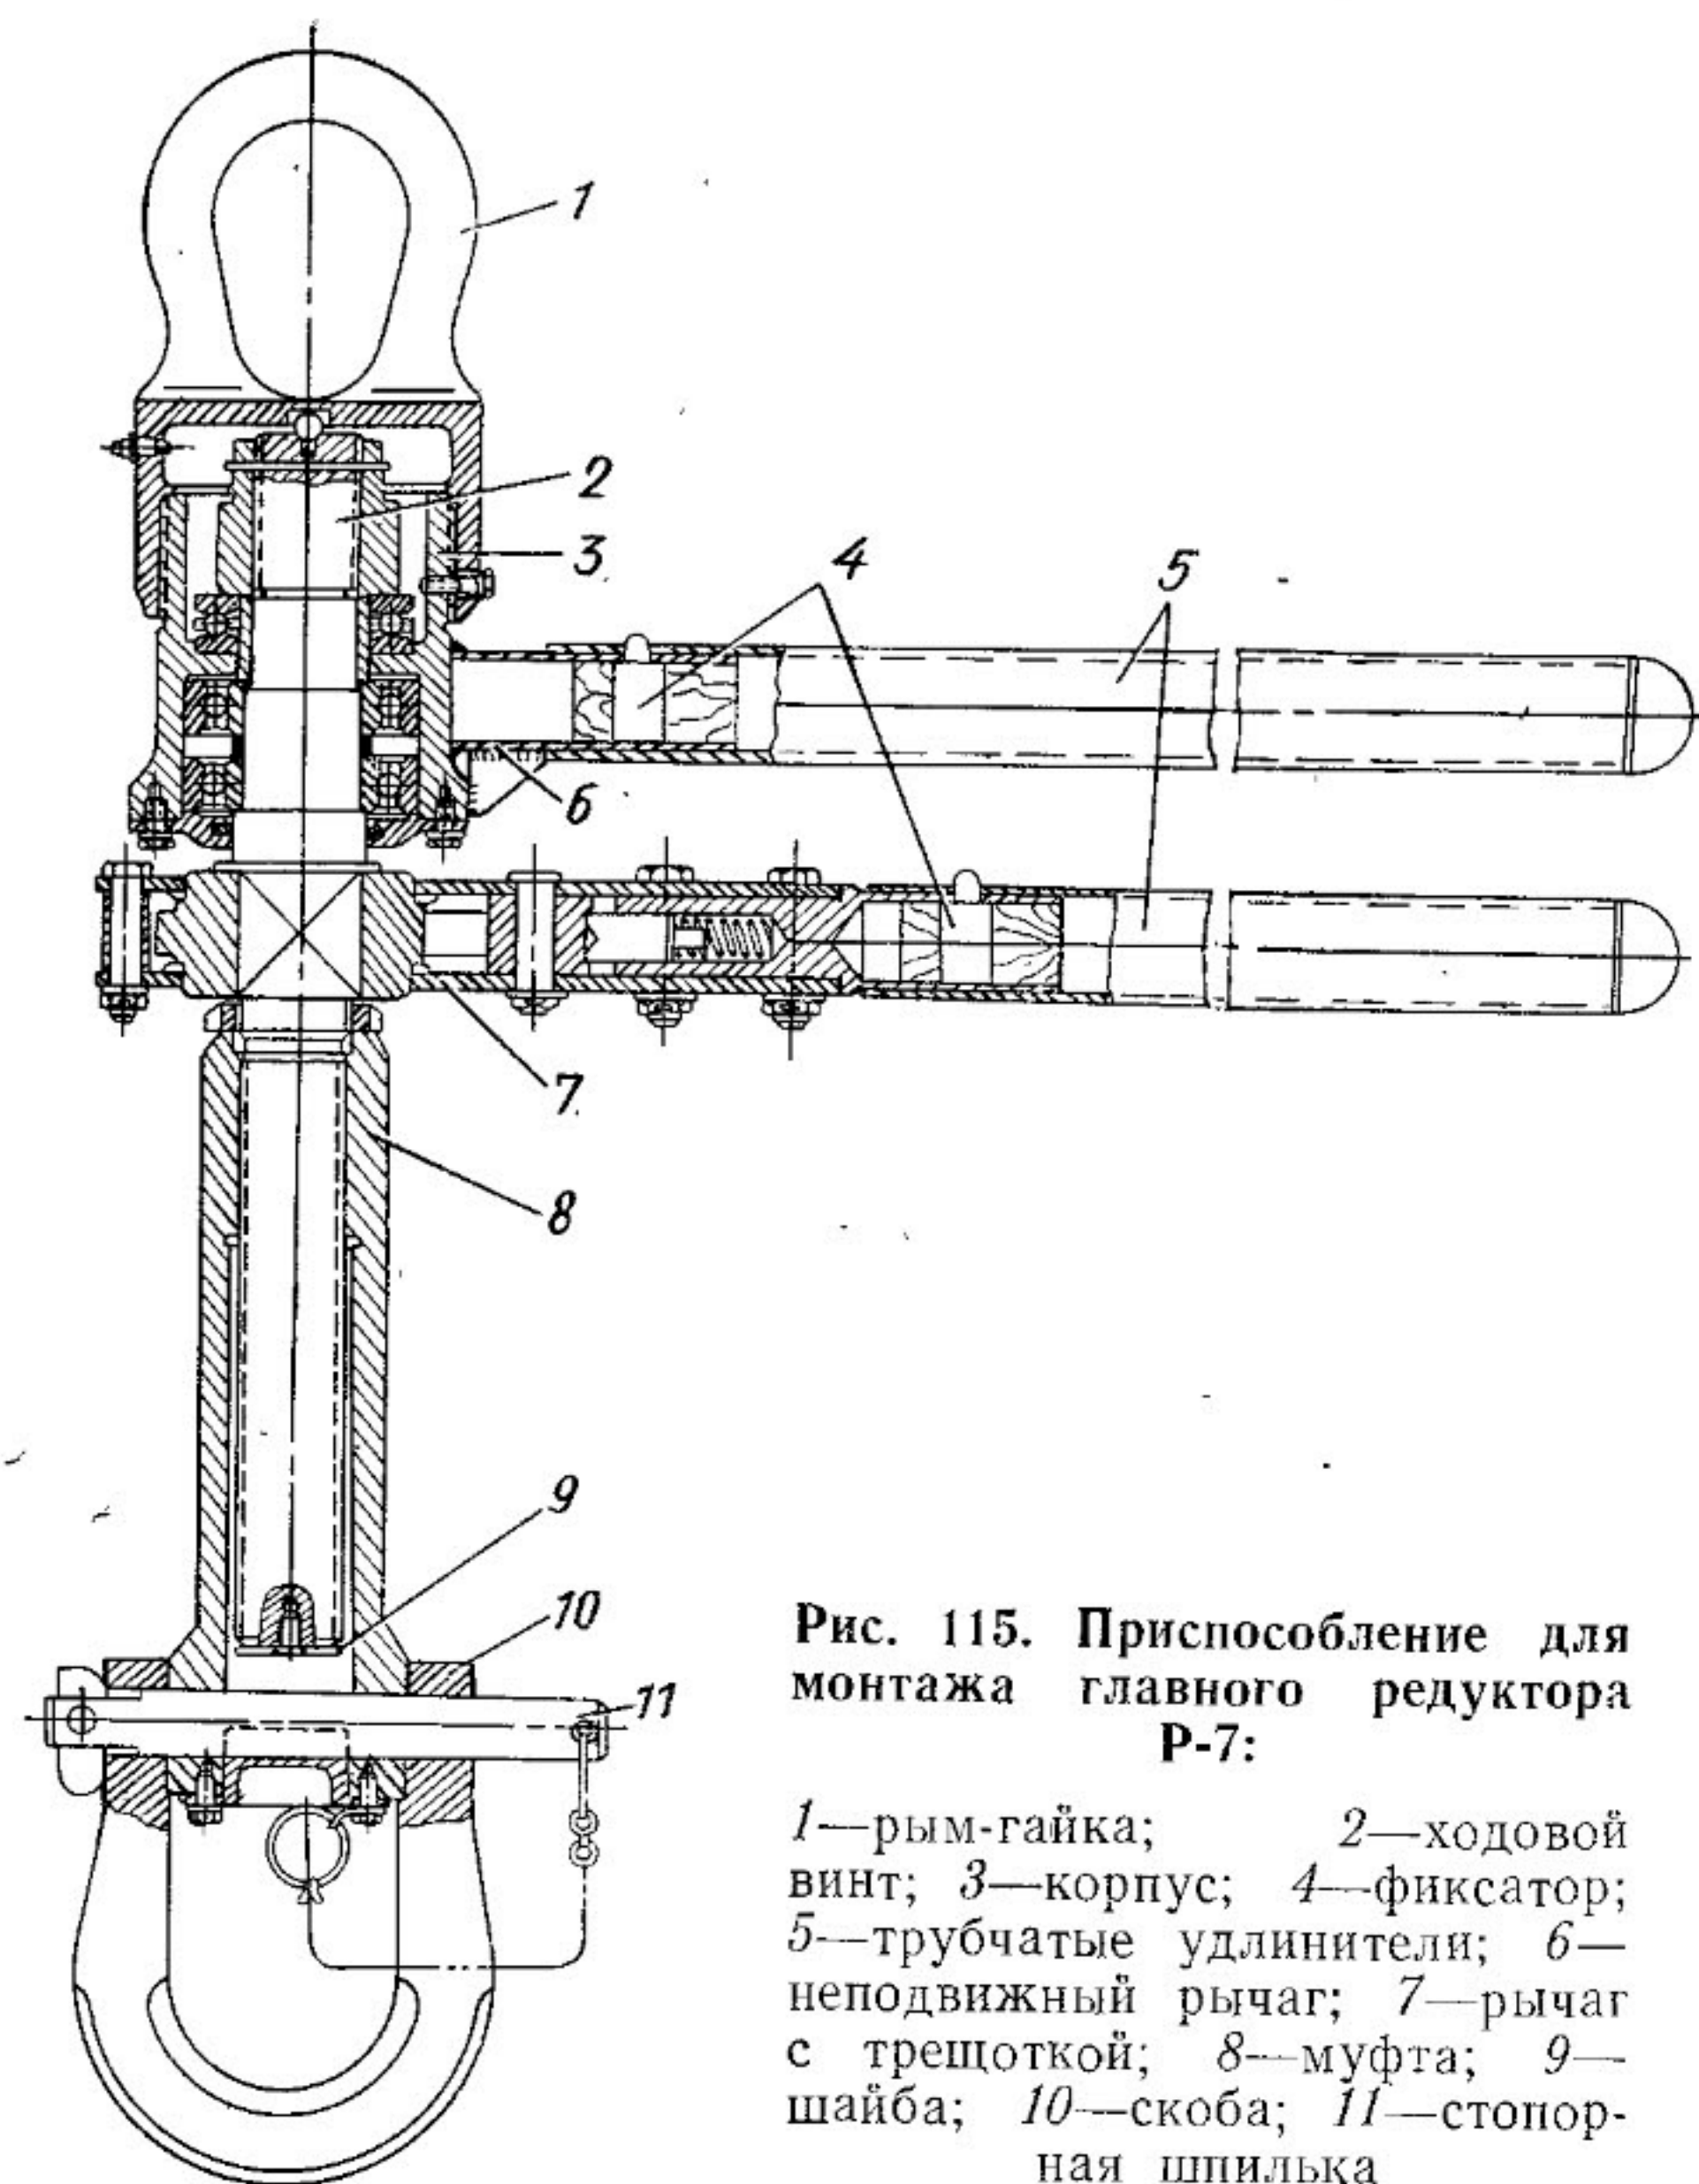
Приспособление для монтажа главного редуктора Р-7:
